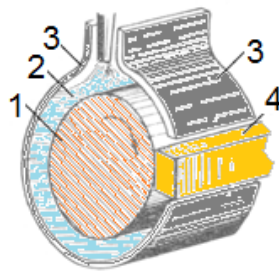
Схема чистової анодно-механічної обробки неметалевим інструментом: 1 – виріб; 2 – електроліт; 3 – катодні пластини; 4 – інструмент для зняття плівки
